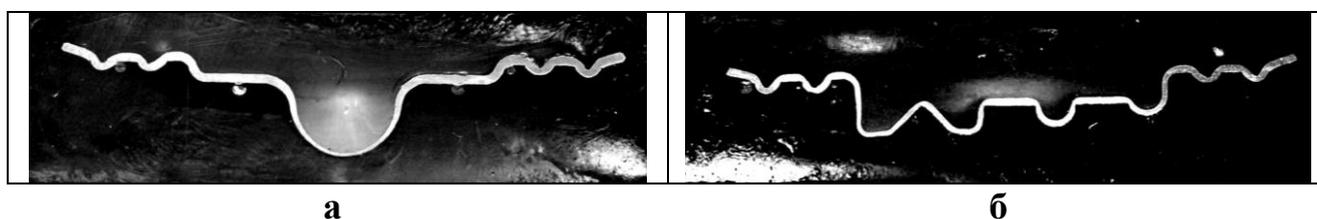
Примеры сечений образцов: а – округлой формы при позитивной формовке; б – более сложной конфигурации при негативной схеме формовки
